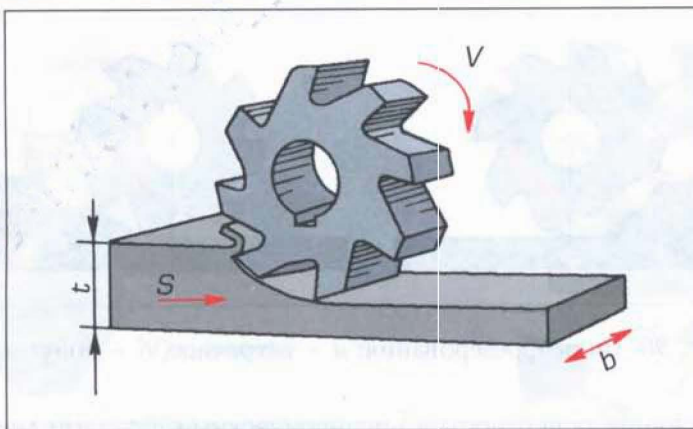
Схема фрезерования:  $t$  – глубина фрезерования (толщина снимаемого слоя материала),  $b$  – ширина фрезерования,  $V$  – скорость резания,  $S$  – направление подачи заготовки
